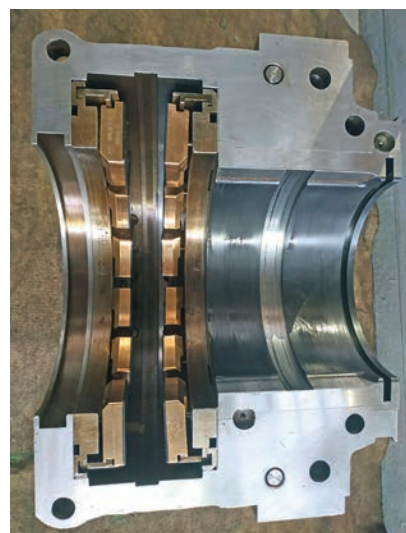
Опорно-упорный подшипник ротора турбины низкого давления после 6284 ч эксплуатации
